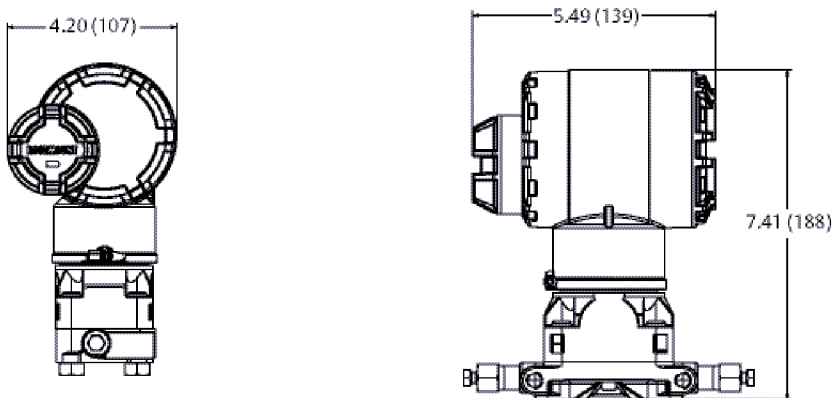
Rosemount 2051C Coplanar Flansch
